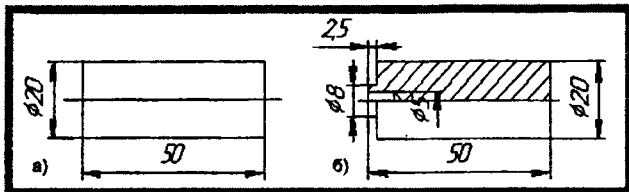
Образцы для проведения испытаний на фреттинг-коррозию
